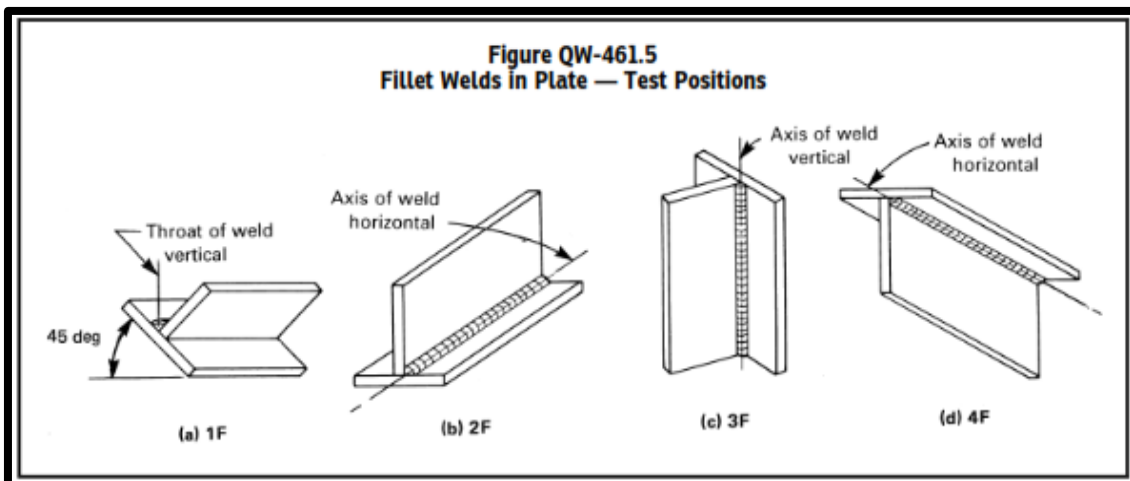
QW-461.5 Soldaduras de filetes en planchas – posiciones de ensayos. Tomada del estándar ASME sección IX
